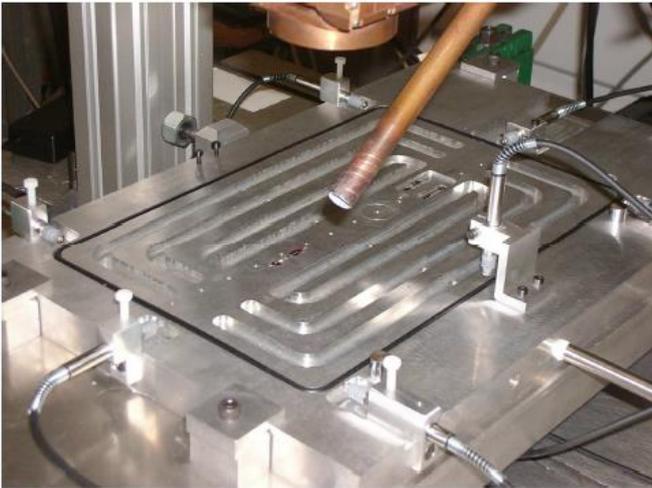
Outillage à dépression utilisé pour les expériences de soudage laser [R1]
